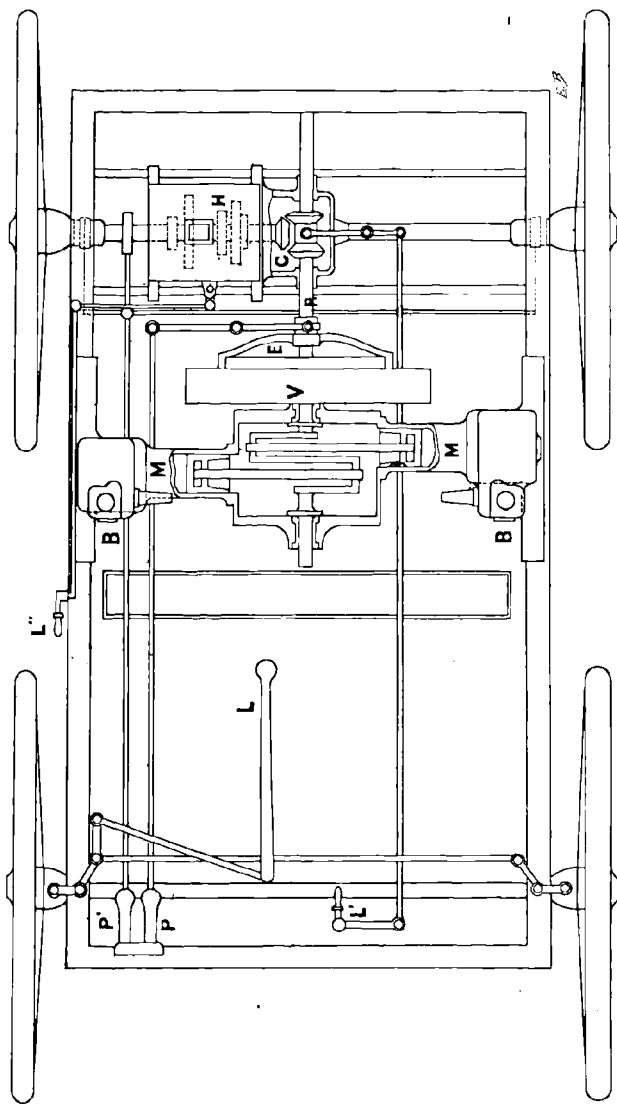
Plan de la voiture Gauthier-Wehrle.
